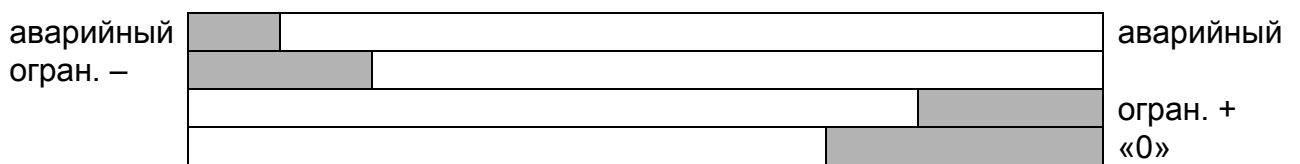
Схема упоров на перемещение фрезерной головки Z
